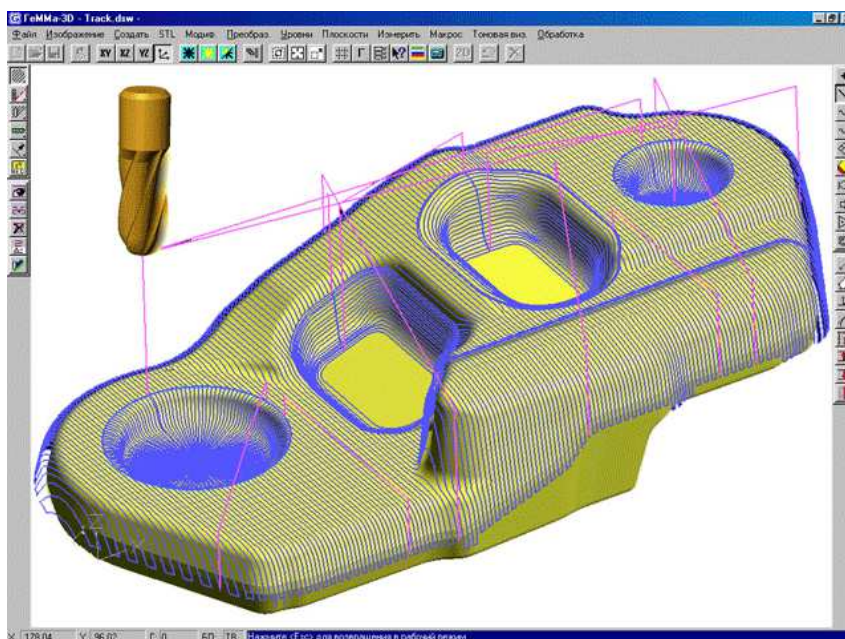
Фрезерна обробка в режимі 3D
